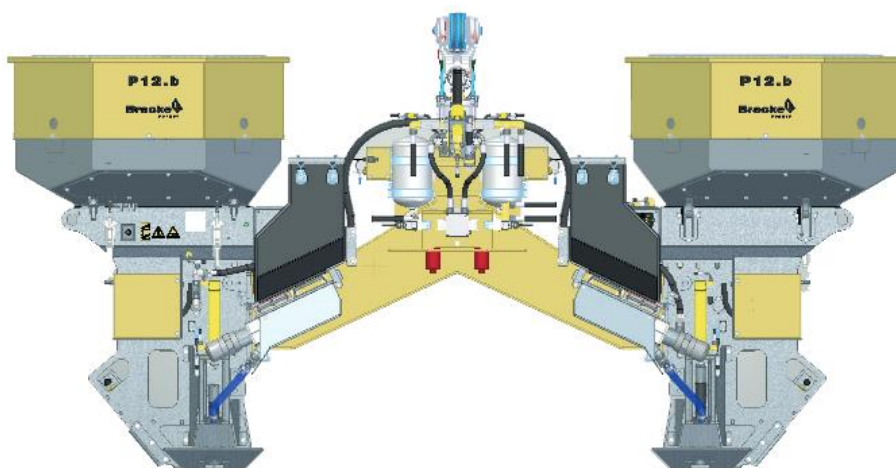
Sázecí hlavice Risutec Oy ASP-720 [34]
